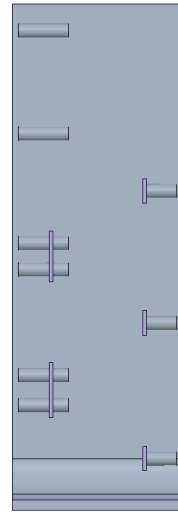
Columna media con torretas de atornillado (corte).
